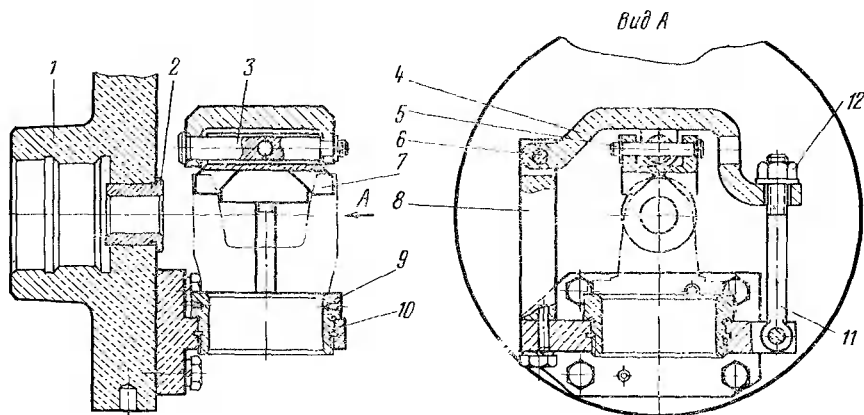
Приспособление для расточки отверстий в вилках под подшипники крестовины карданного вала:
